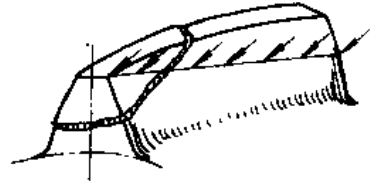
斜齿圆柱齿轮轮齿受载及折断
